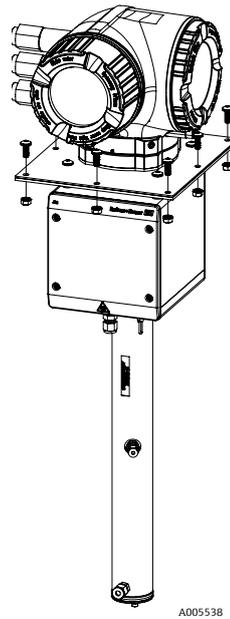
Halterung für Montage auf einem Befestigungsblech und Befestigungsmaterialien
